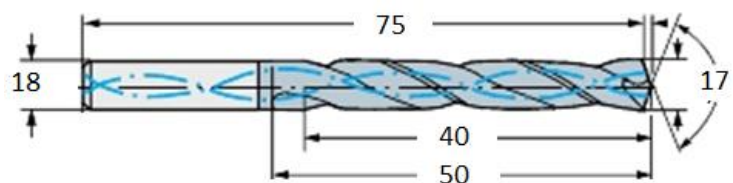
Сверло Sandvik Coromant CoroDrill 460.1-1700-128A1-ХМ GC34
